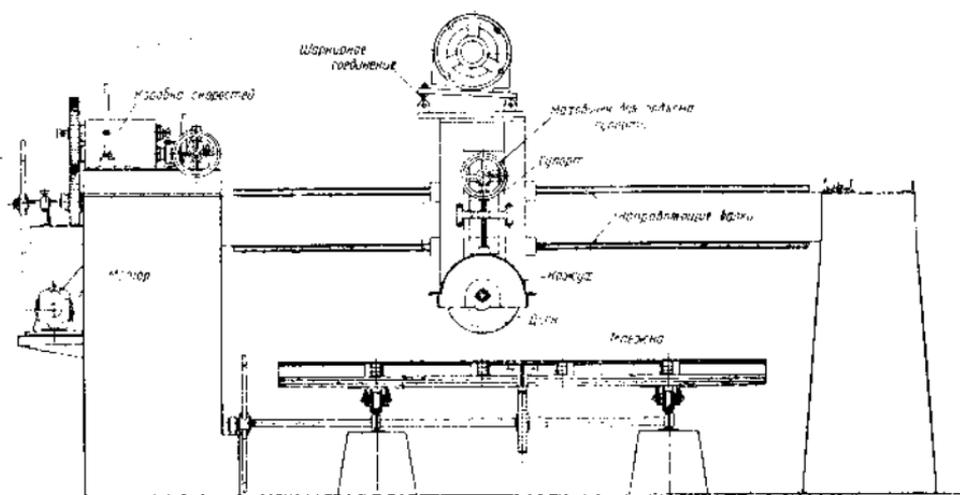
Фрезерный станок «Торпедо» советской конструкции инж. Ф. Ф. Шмидта
